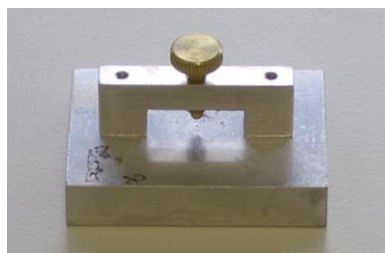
Werkzeuge zur Erzeugung des mechanischen Drucks beim Bonden
